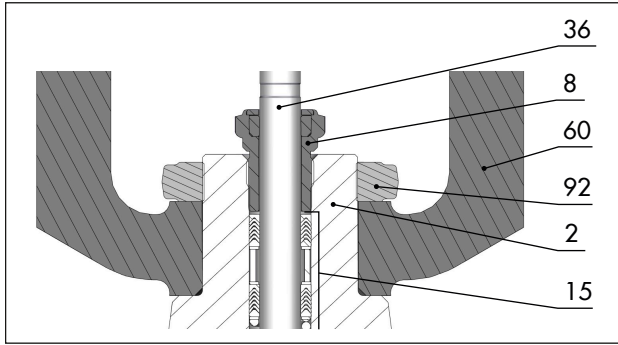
Packung mit Gewindebuchse zentral verschraubt (Beispieldarstellung)
